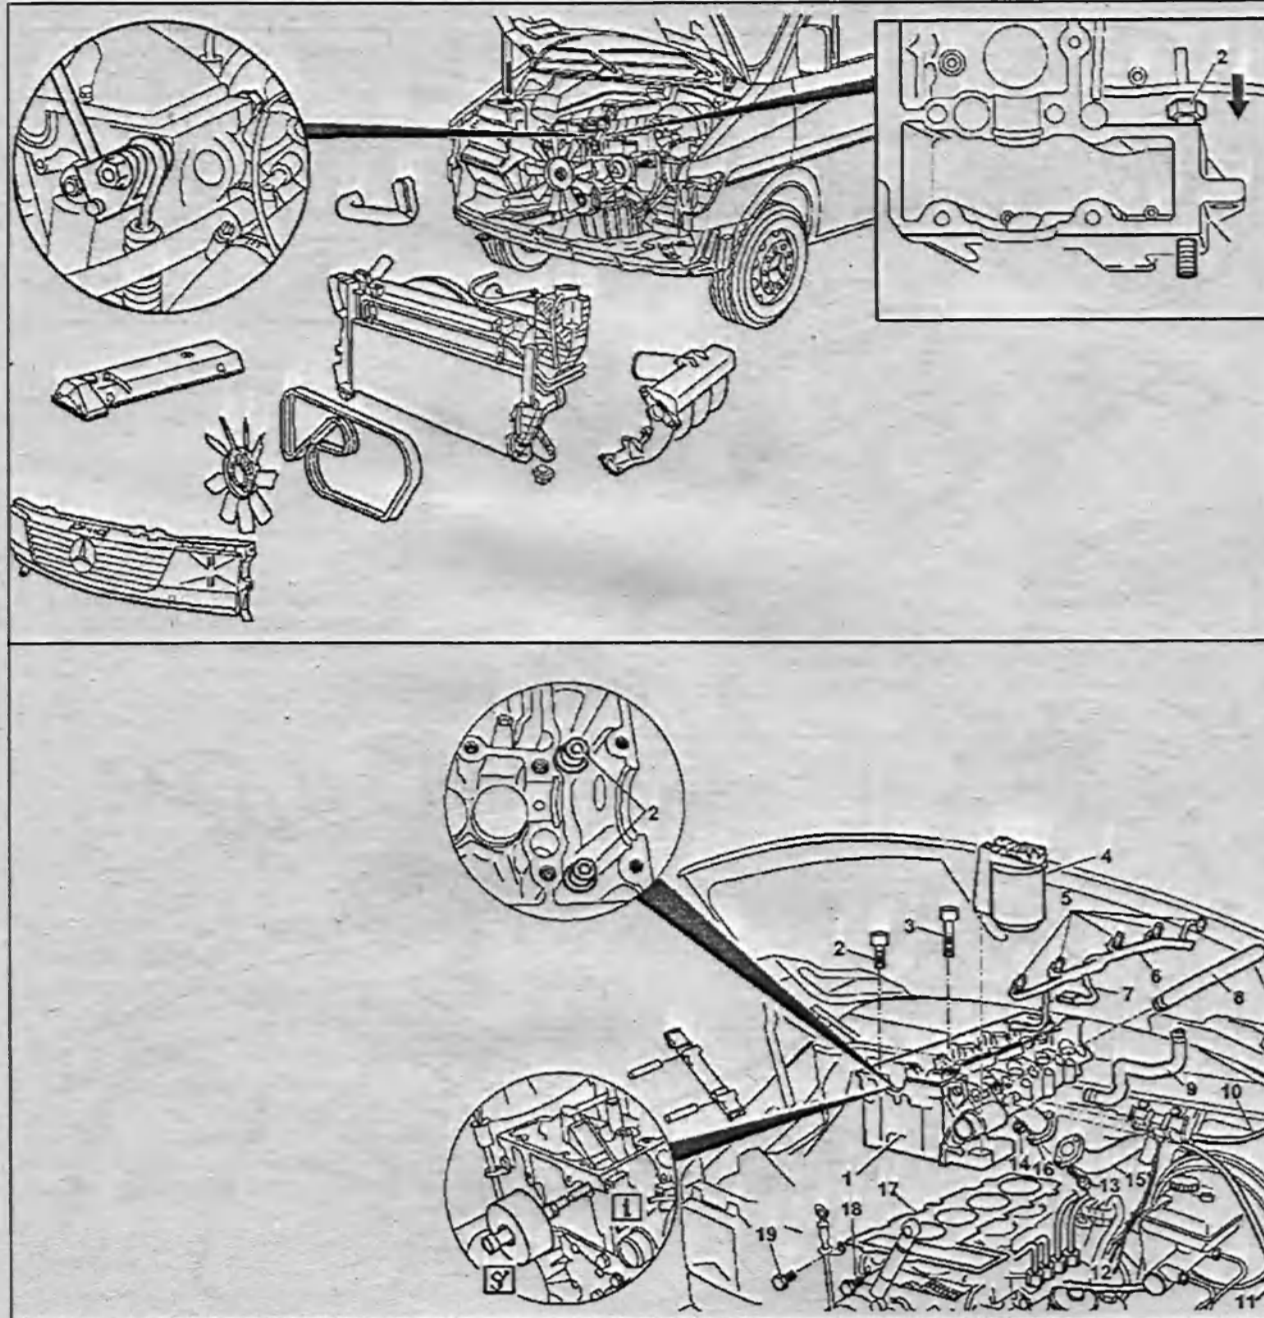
Головка блока цилиндров двигателя 601.943:
